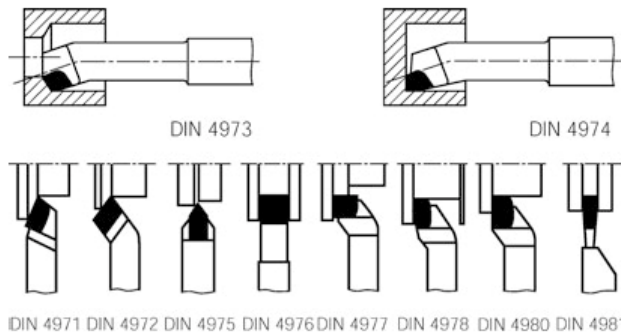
Werkzeugformen beim Drehen für verschiedene Bearbeitungsaufgaben / Geometria sculelor de strunjit cu plăcuțe din carburi metalice
